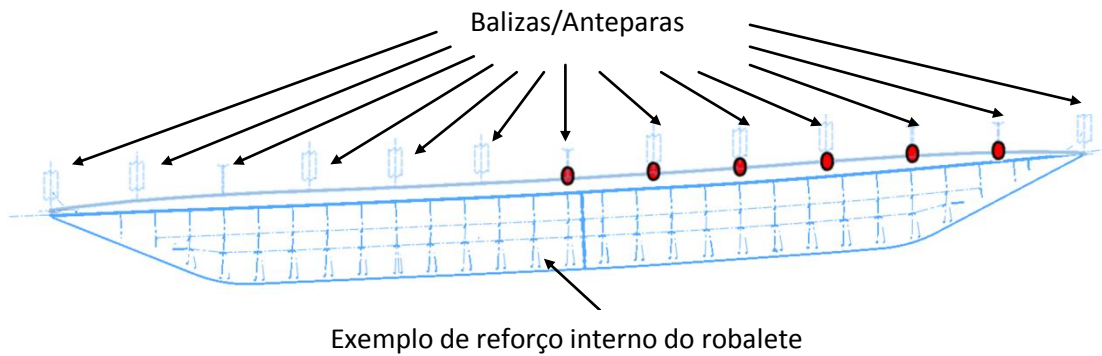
Vista geral, exterior, do robalete. Localização das fissuras registadas (pontos a vermelho).
